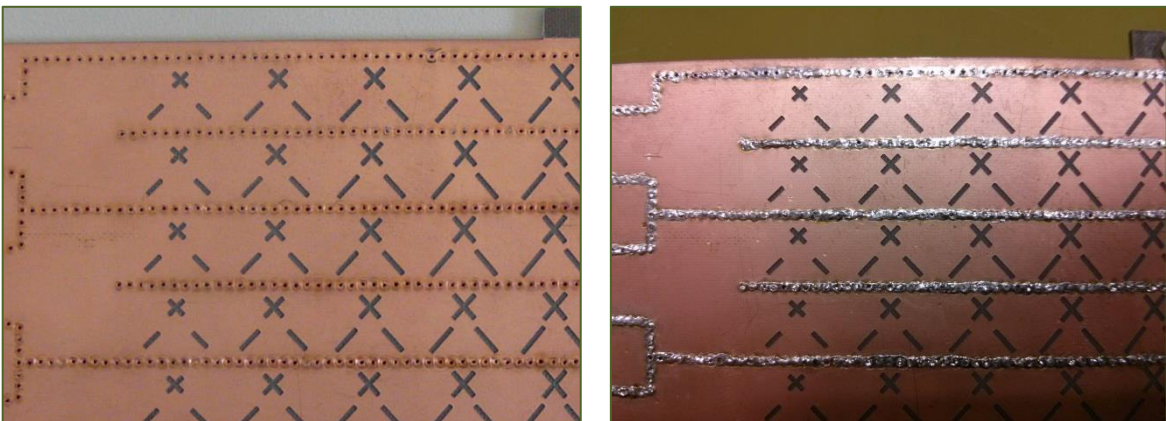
Detalle de elementos radiantes y vías antes de la metalización (izquierda) y tras la soldadura de los remaches (derecha)
